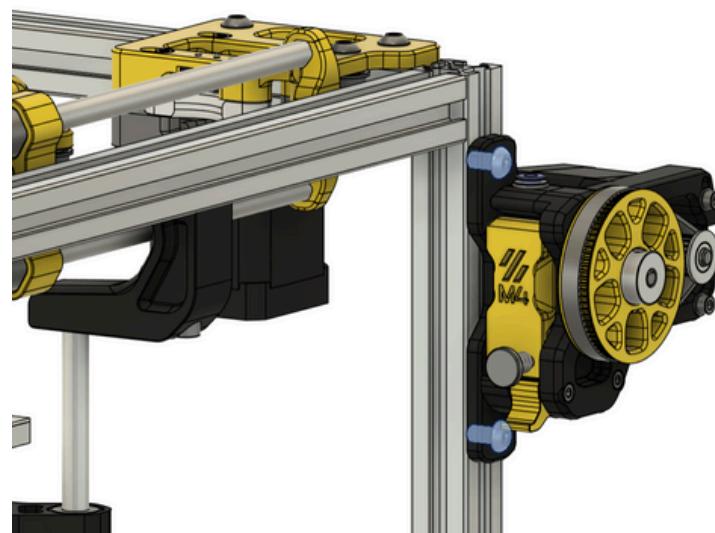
Vista del extrusor posicionado en la estructura de aluminio.
